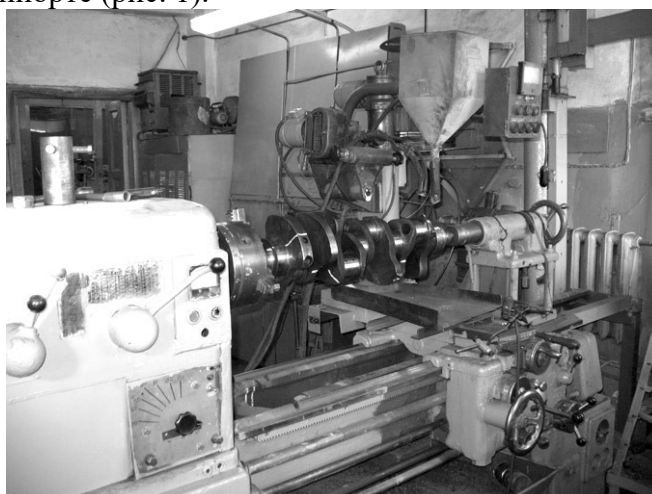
Общий вид переоборудованного токарного станка для наплавки шеек коленчатых валов
